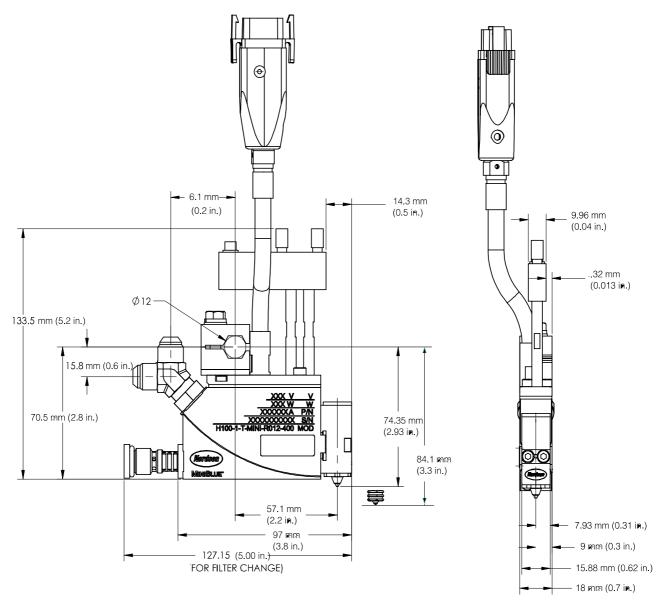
Dimensions d'un pistolet mono-module ultra-plat à électrovanne SD
